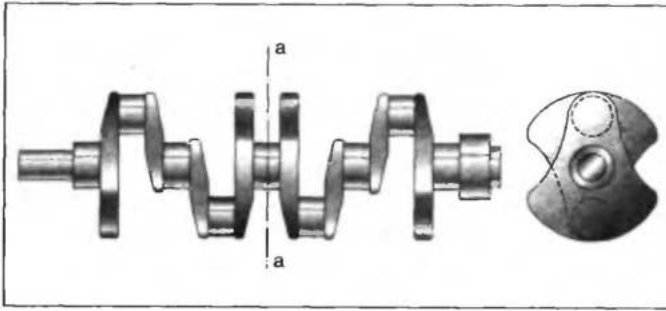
Коленчатый вал рядного четырехцилиндрового двигателя с одинарными противовесами:
